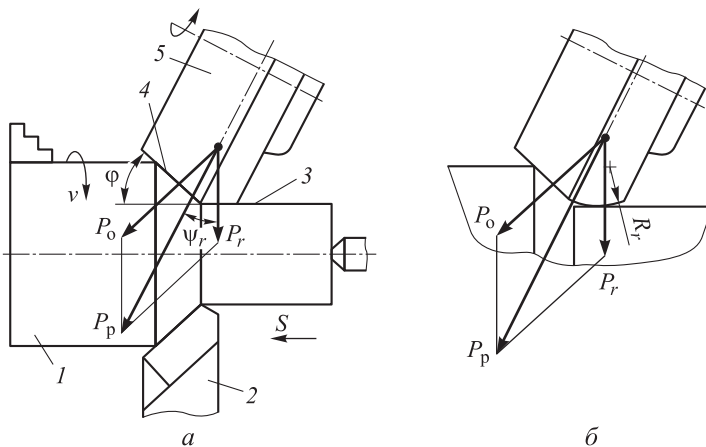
Схема обработки при упрочнении роликом с двумя рабочими поверхностями: 1 — заготовка; 2 — резец; 3 — обработанная поверхность; 4 — поверхность резания; 5 — накатной ролик; дополнительная поверхность ролика с линейной образующей (а), с профильным радиусом (б); P_p — результирующая нагрузка ОПД на заготовку; P_o — нагрузка ОПД на поверхность резания; P_r — радиальная составляющая нагрузки ОПД, действующая на обработанную поверхность
